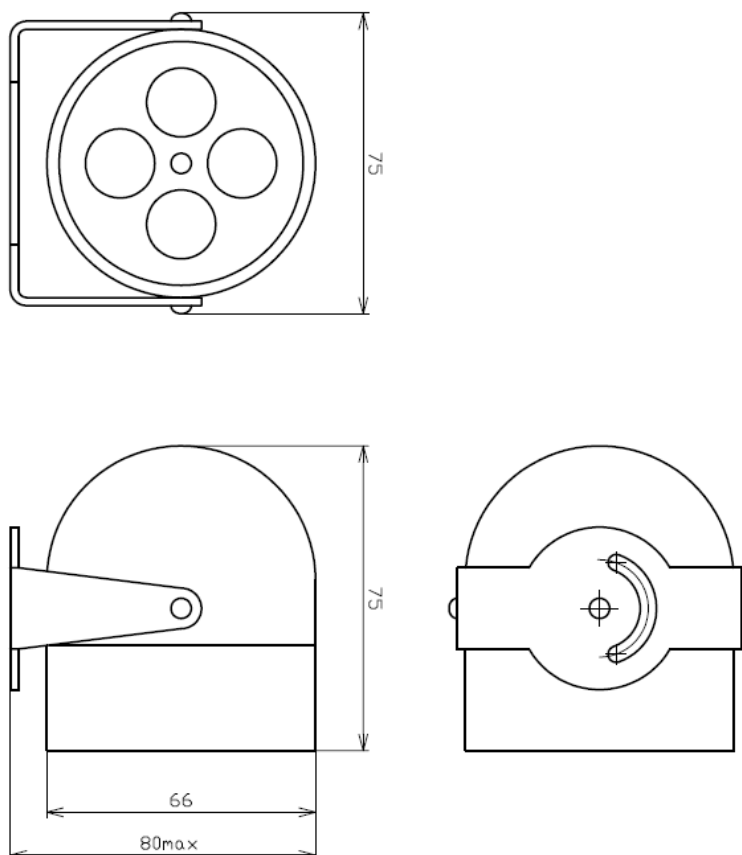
Габаритный чертеж прожектора ИК-601-40.
